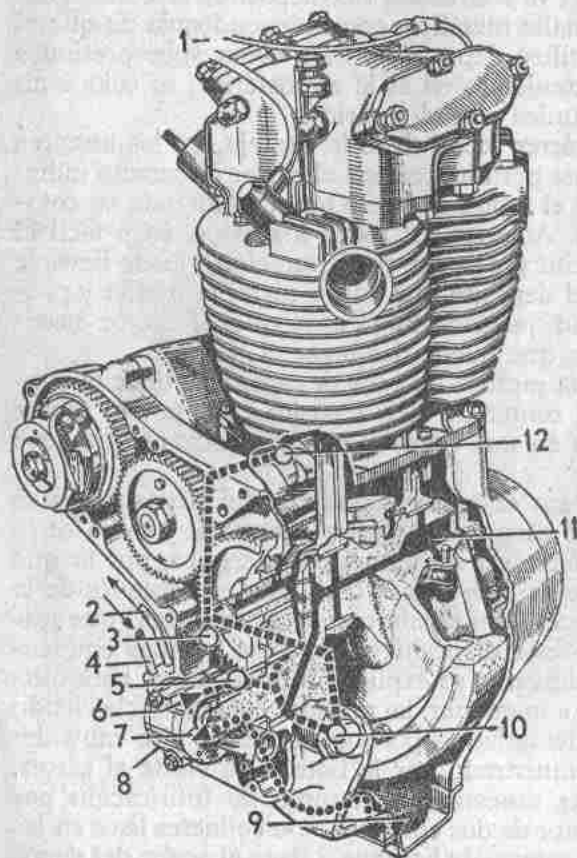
Engrase por cárter seco en un bicilíndrico B. S. A.
